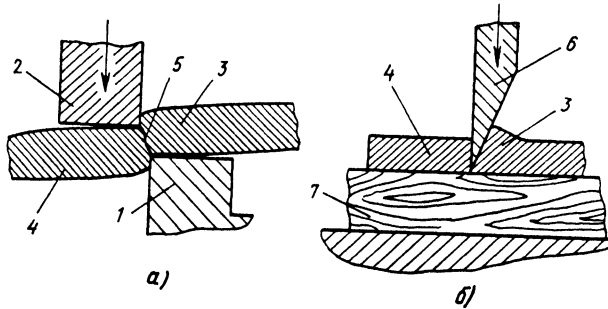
Принципиальные схемы разделения сдвигом (а) и пластическим внедрением инструмента (б): 1 - нож неподвижный; 2 - нож подвижный; 3 - разрезаемый листовой металл; 4 - отрезаемая заготовка; 5 - линия раздела; 6 - ножевой пуансон; 7 - подштамповая плита
